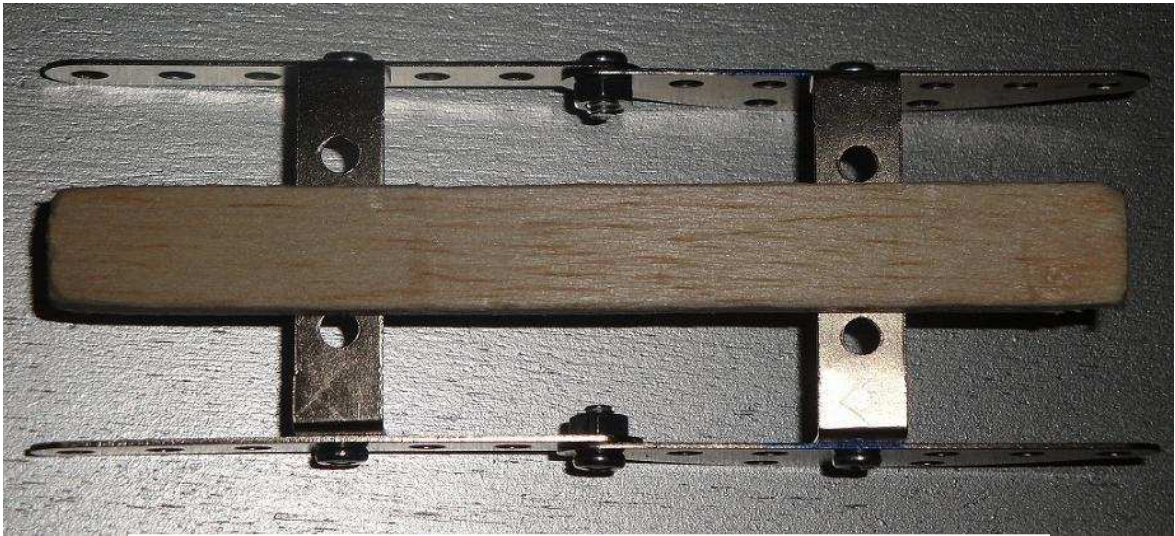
Ubicación de la plancha de madera sobre la estructura metálica.
